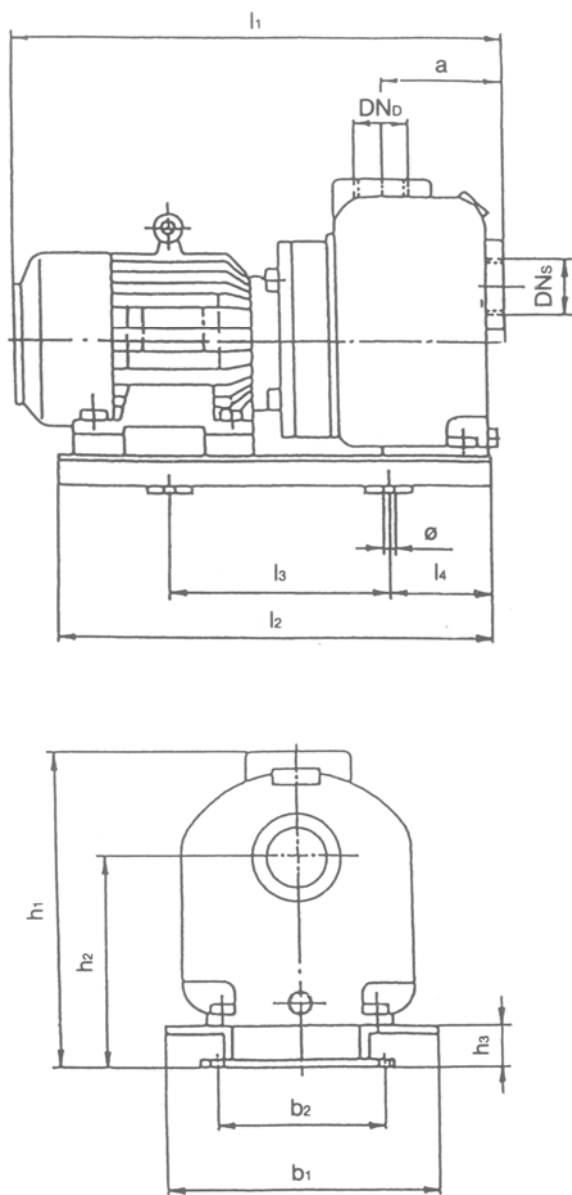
Габаритный чертёж насоса типа PO 32BL,
